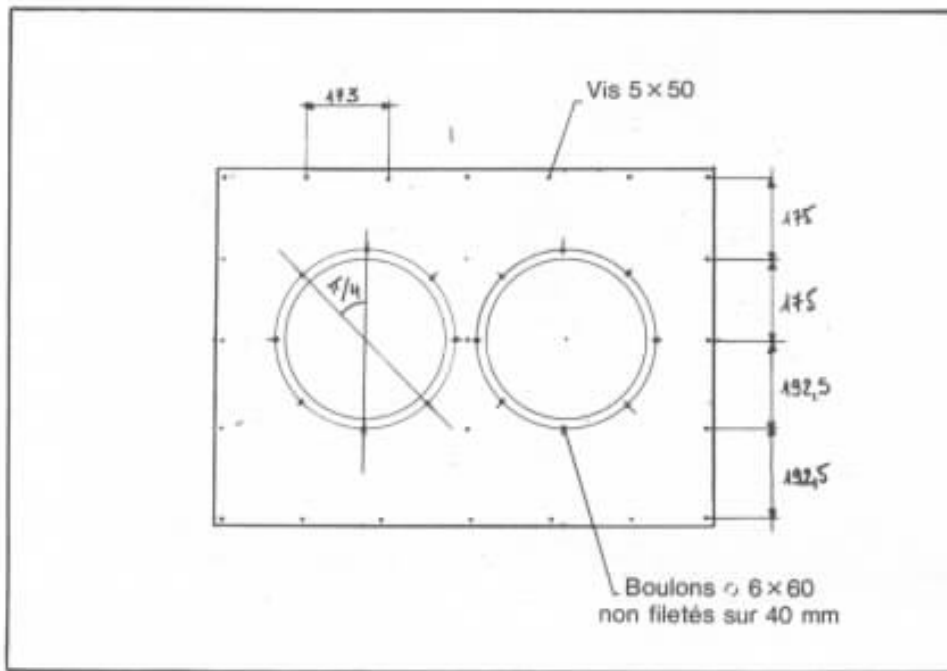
Plan de vissage de la face avant sur les tasseaux de fixation ainsi que positionnement des boulons de maintien des haut-parleurs.
